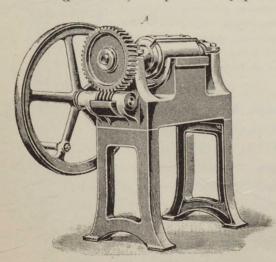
Станокъ для обстрагиванія затылка стерео-
